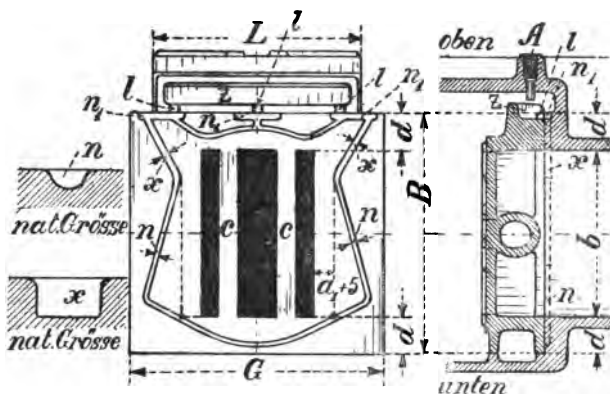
Fig. 761. Grundriss. Fig. 762. Querschnitt.
